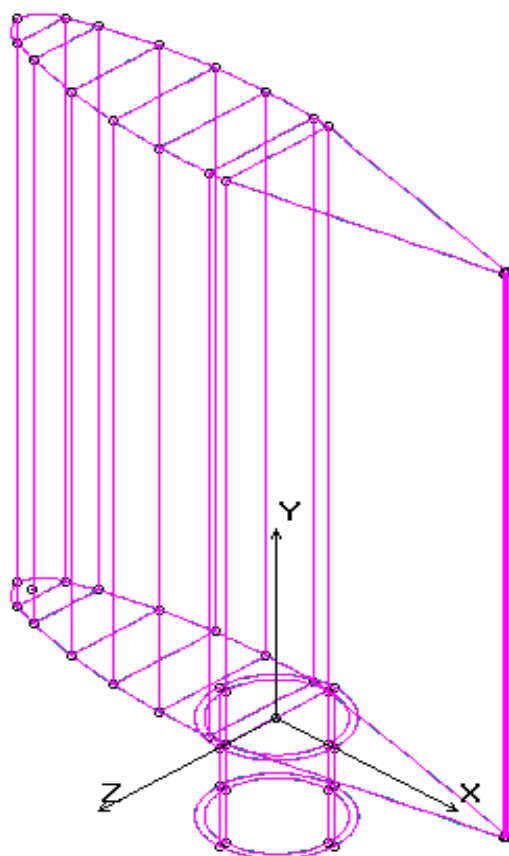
Поверхности объемного тела лопатки НА и нижнего подшипника
